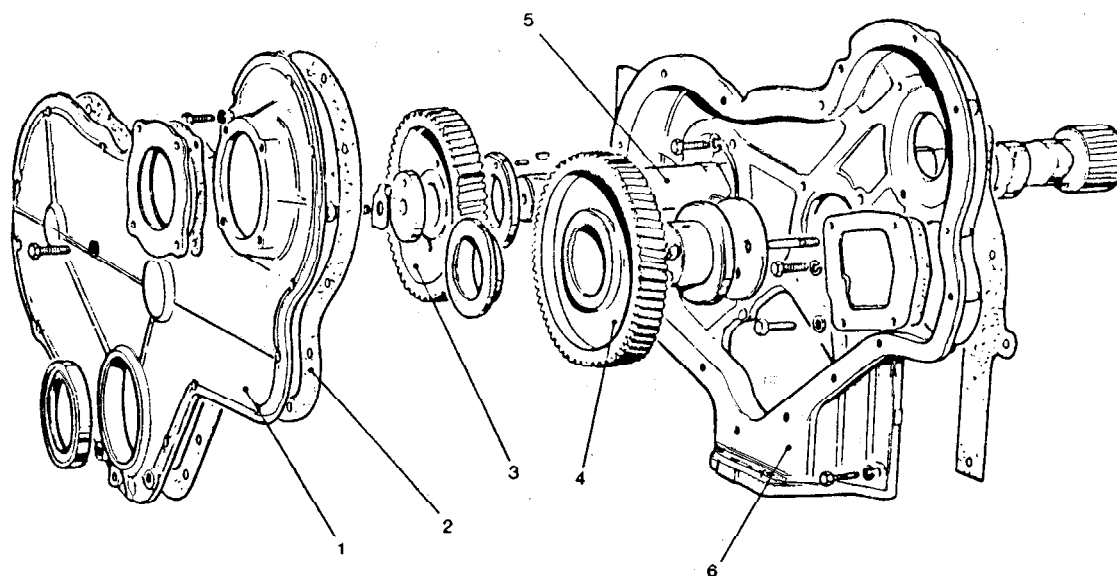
Caja y tapa de engranes de sincronización: 1 tapa, 2 junta, 3 engrane de sincronización, 4 engrane de mando de auxiliares, 5 árbol de levas, 6 caja PERKINS
